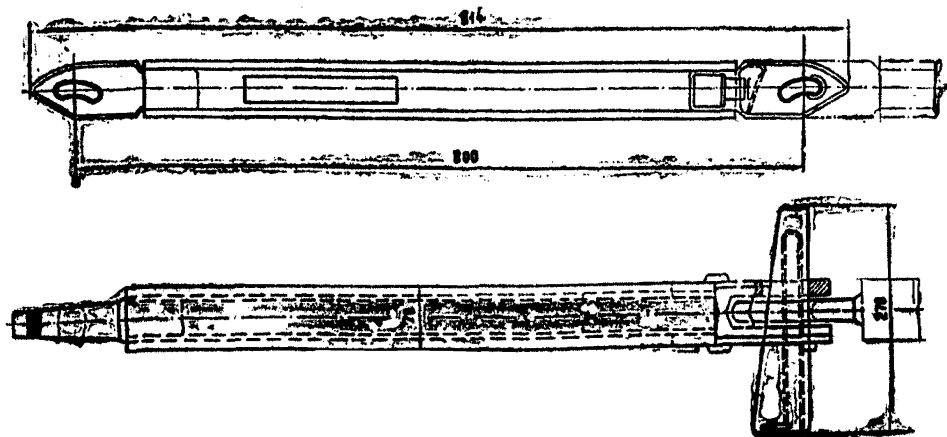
Конструкции металлических шарнирных верхняков:
